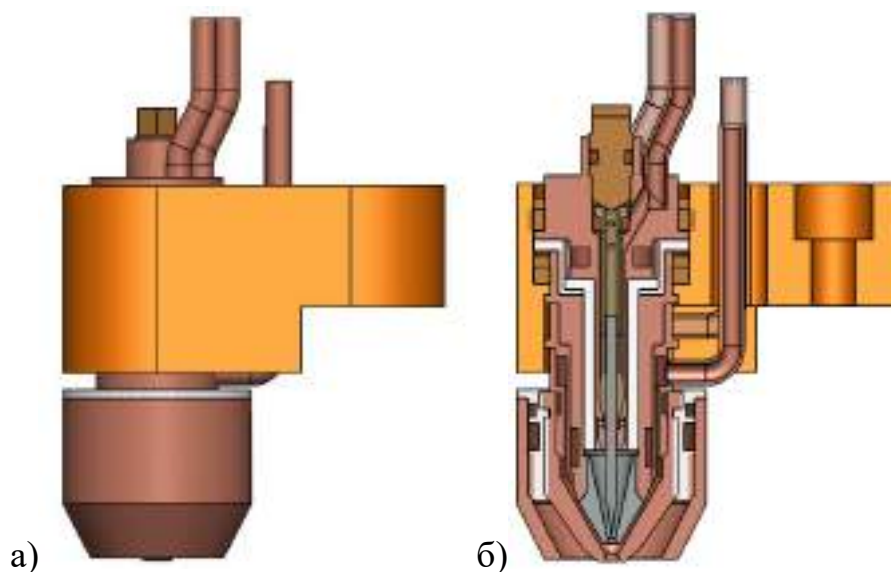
Загальний вигляд (а) та поперечний переріз (б) плазмотрона для адитивного плазмового порошкового наплавлення з транспортуючим соплом.
